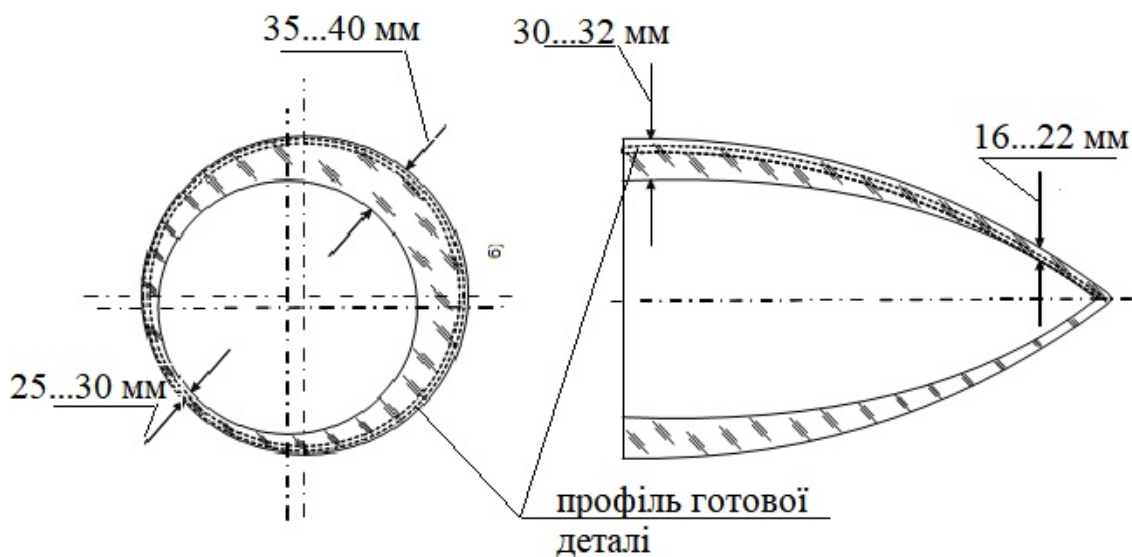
Схема відхилення профілю заготовки від профілю готового виробу
